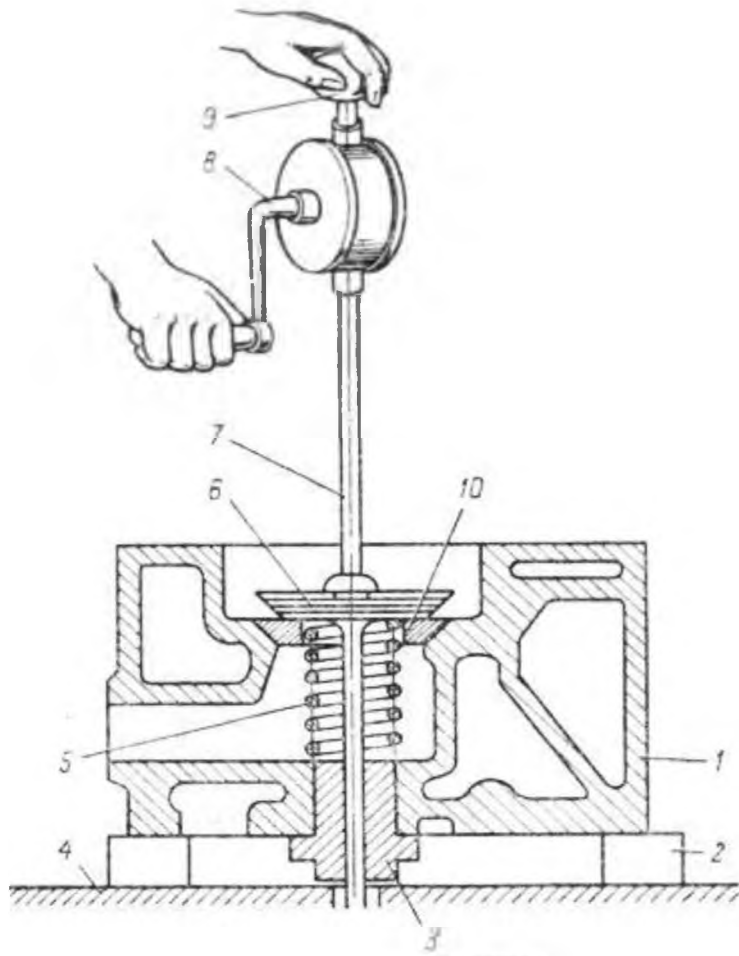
Универсальное приспособление для доводки отверстий в деталях
